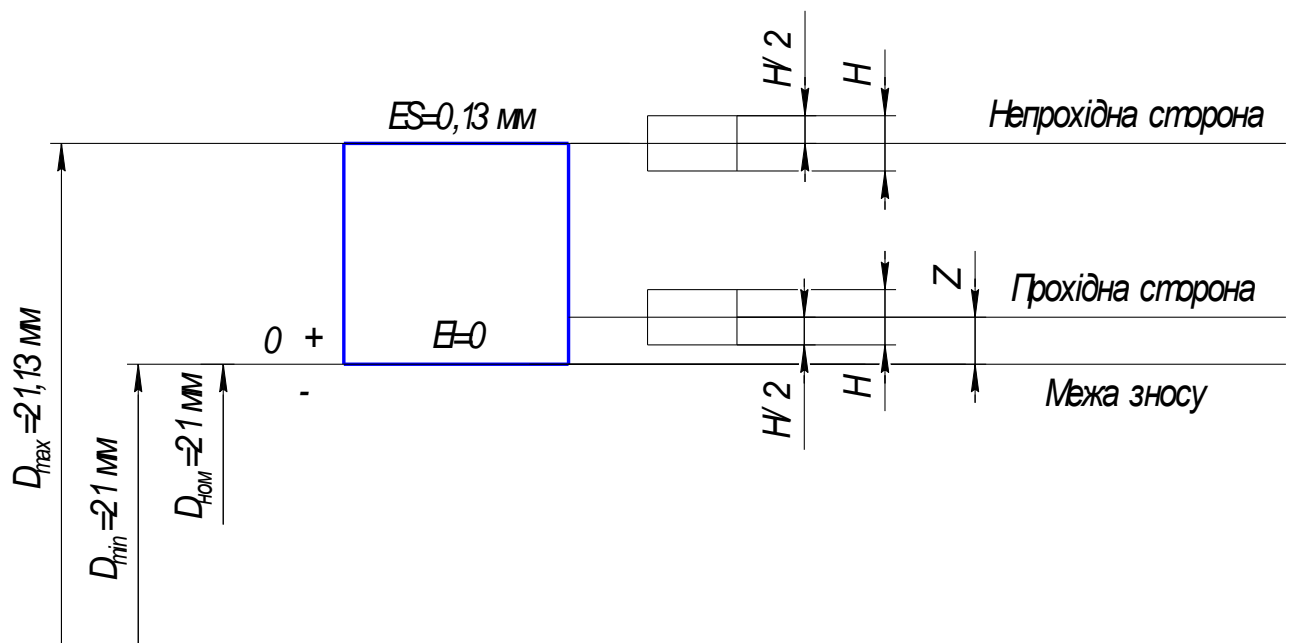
Схема розташування допусків робочих поверхонь калібрів для контролю розміра $\varnothing 21H11(^{+0,13})$
